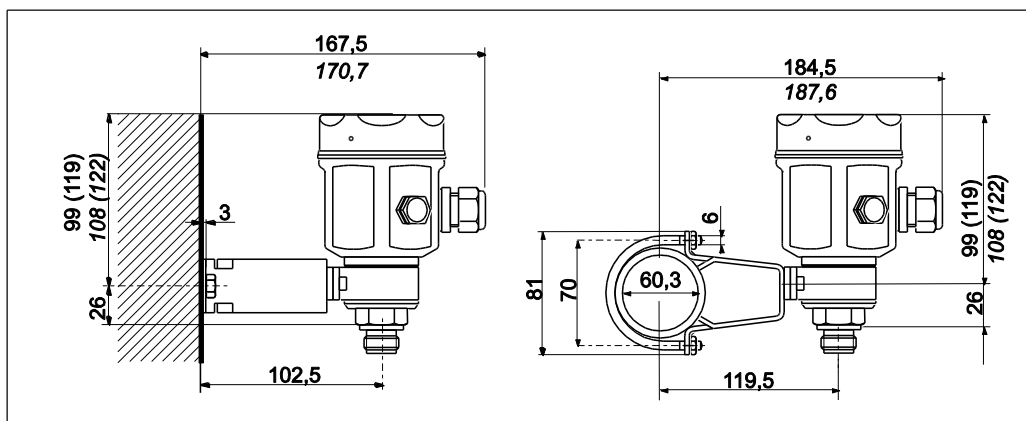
Монтаж прибора PMP41 на стене или трубе
